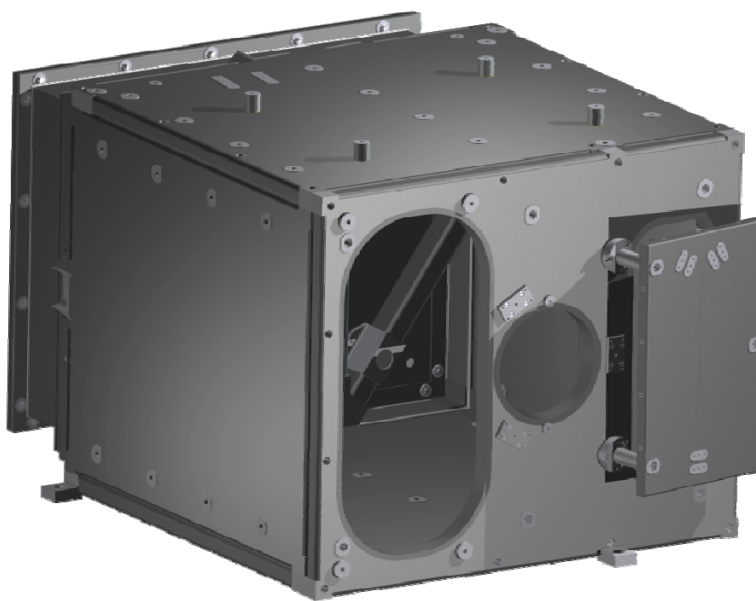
Загальний вигляд ТРС корпусу оптичного СВР3 панельного типу
